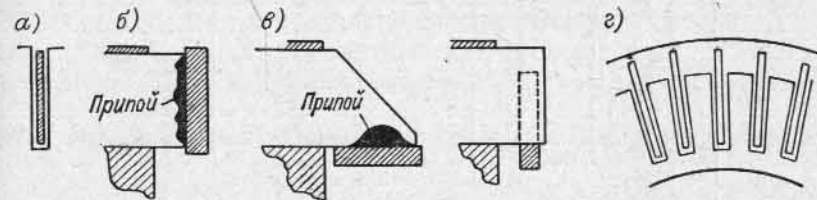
Конструктивные детали ротора асинхронного двигателя с глубокопазом
